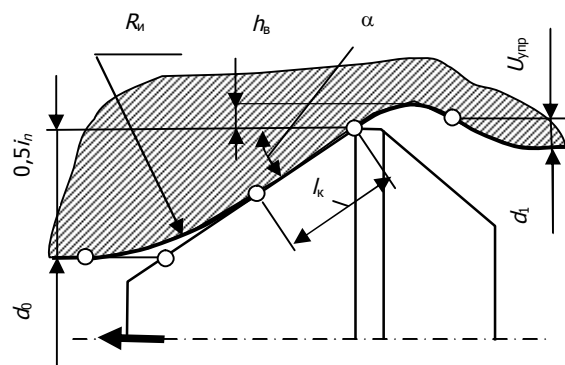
Схема очага деформации трубчатой заготовки при дорновании отверстия
